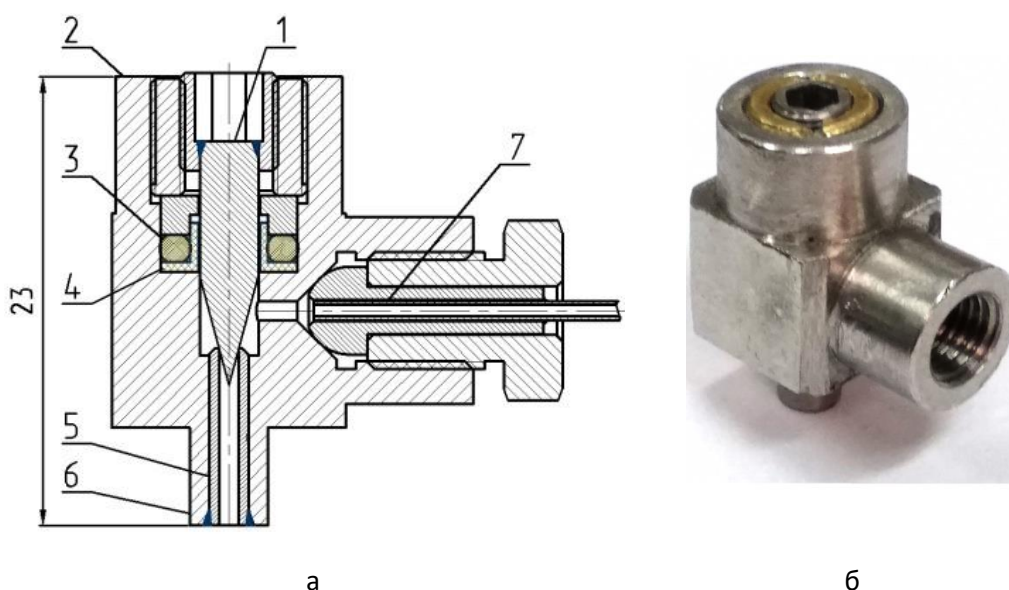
Конструкция (а) и внешний вид (б) вентиля
